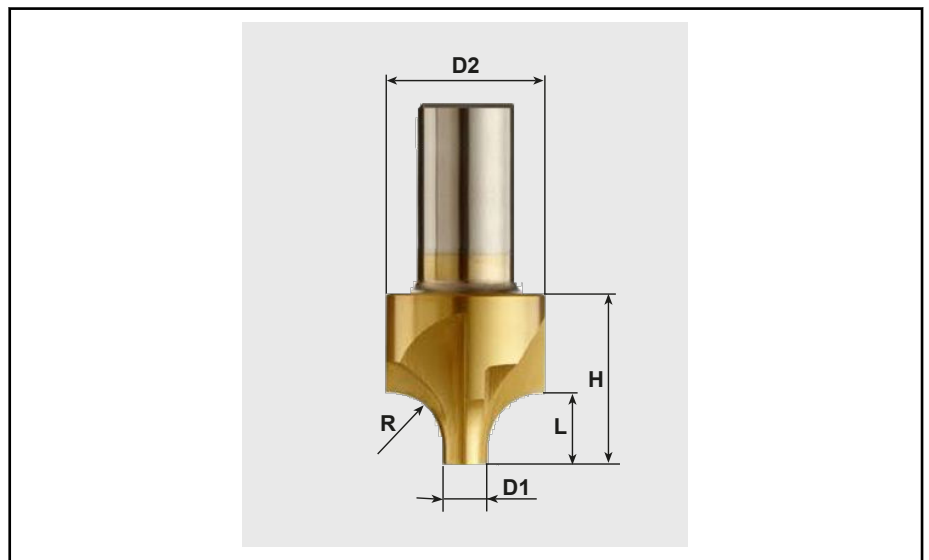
Werkzeugbeschreibung TOOL/CRMILL Viertelrund-Profilfräser
